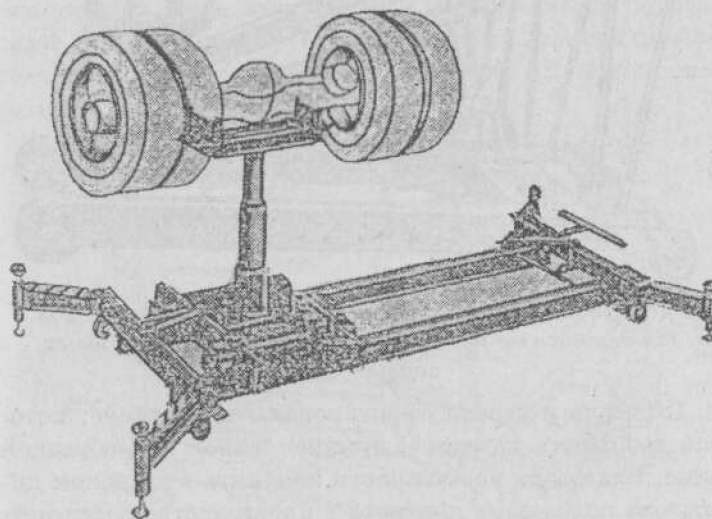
Общий вид устройства П 248 для замены агрегатов автомобилей
